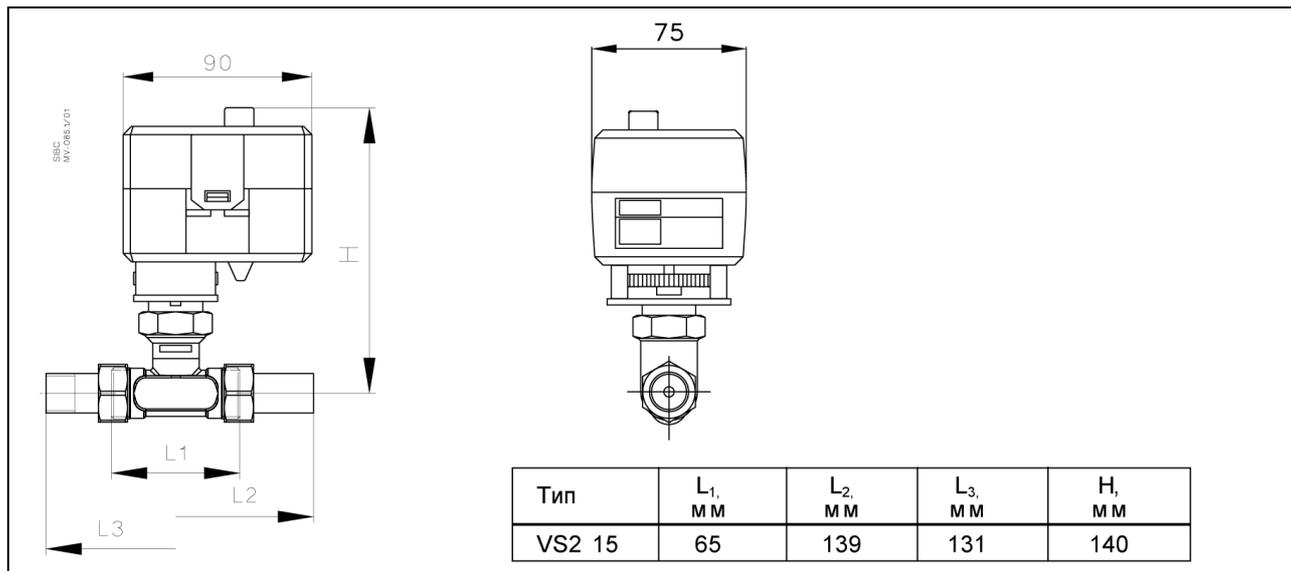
Габаритные и присоединительные размеры AMV 100 с клапаном VS2.
